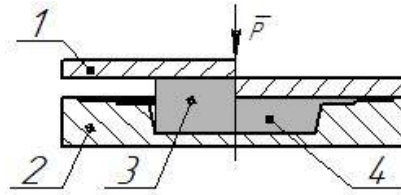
Схема гарячого деформування: 1- бойок; 2 - матриця; 3 - заготовка; 4 – поковка
